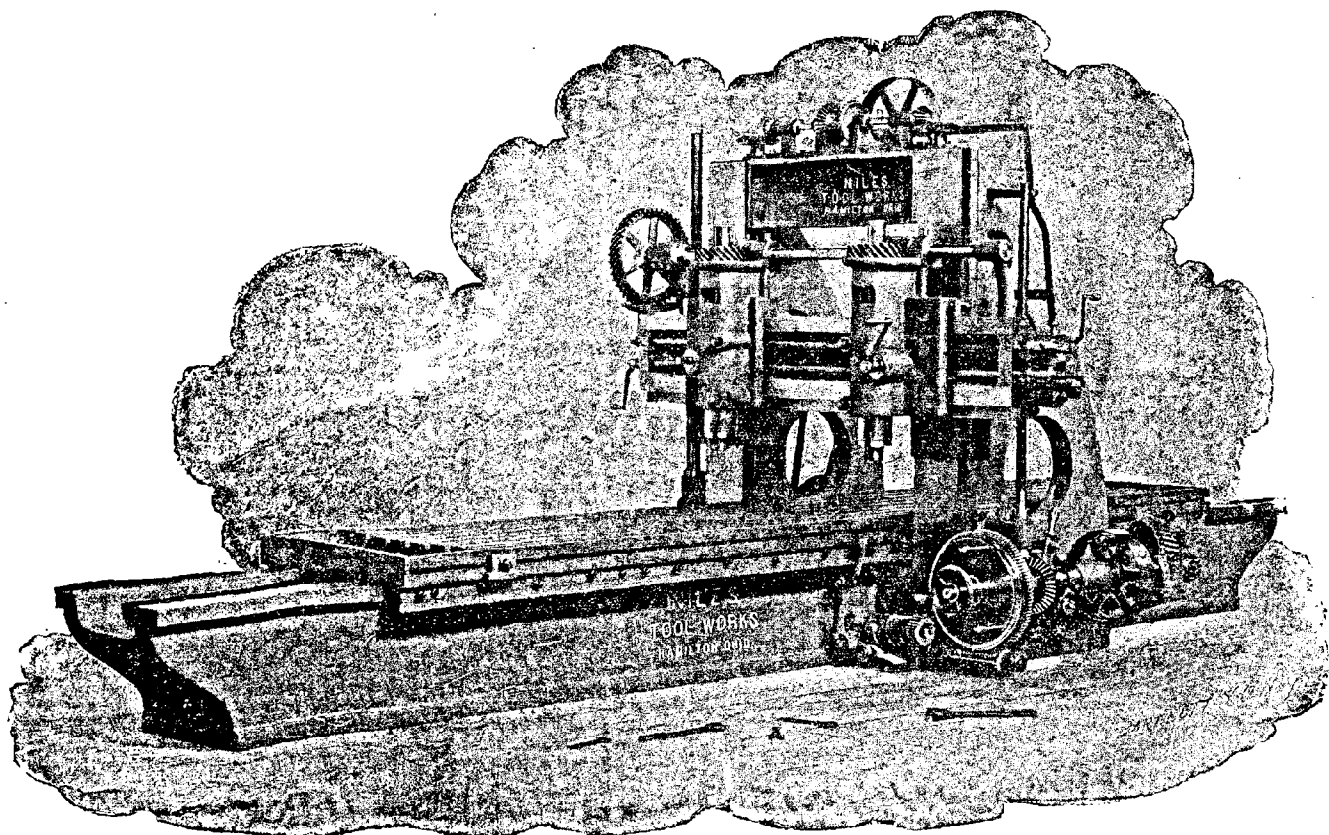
Machine à traîner verticale Niles genre raboteuse à deux porte-fraises.
